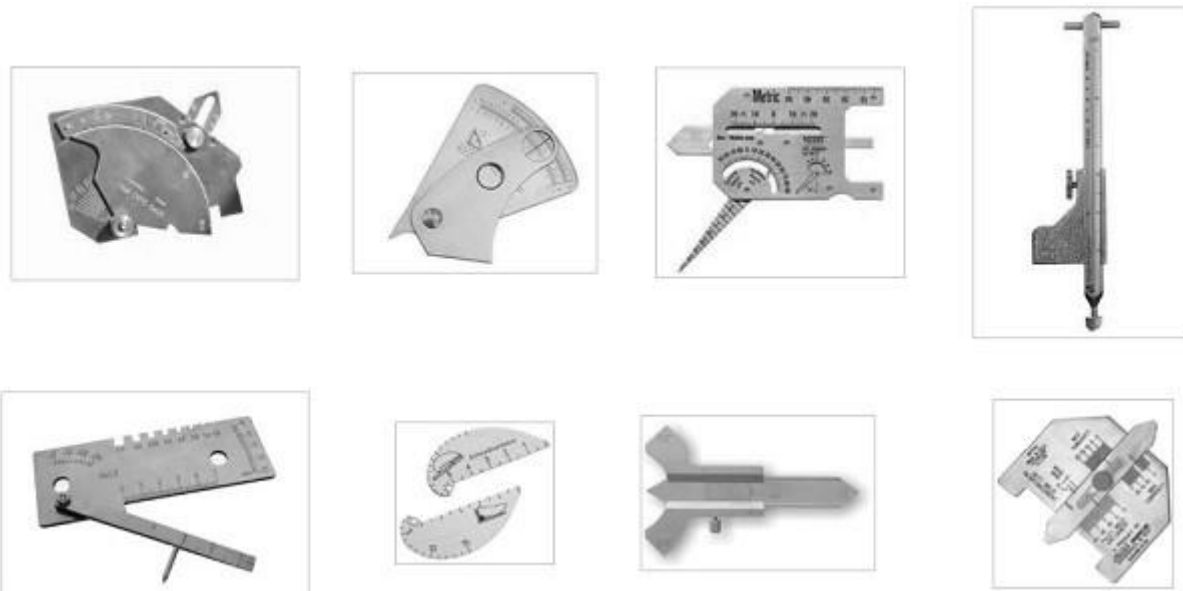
Примеры шаблонов, применяемых при измерительном контроле качества подготовки под сварку и готовых сварных соединений
